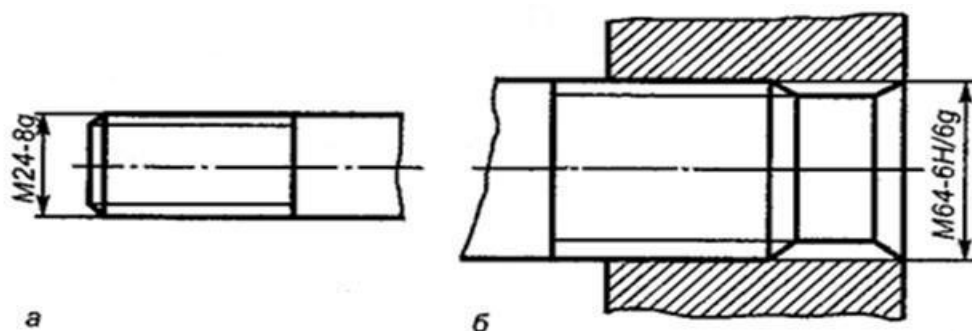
Обозначение поля допуска резьбы
